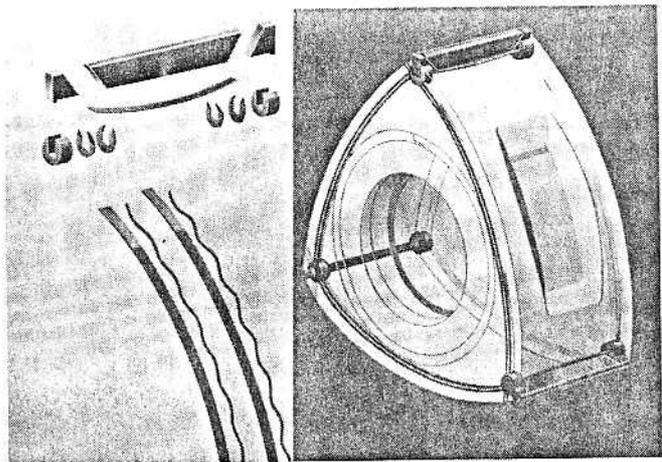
Dichtsystem für Kreiskolbenmaschinen
